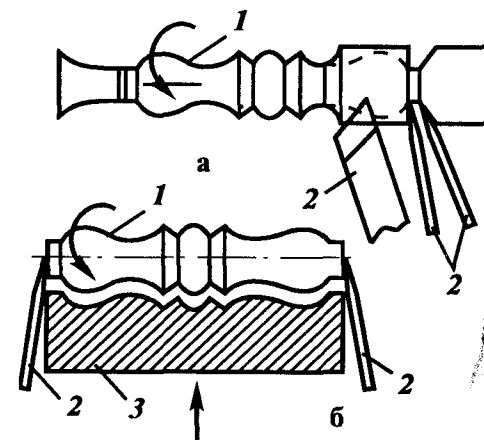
Точение фасонных поверхностей: а — стамеской; б — профильным резцом: 1 — заготовка; 2 — стамеска; 3 — профильный резец
